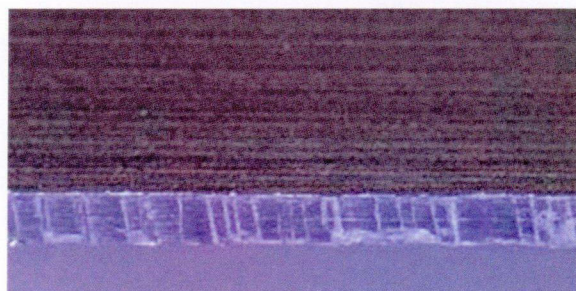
は Table 5-8 に示す加工条件で厚み 2 mm のアルミサッシ(材質 : JIS A4706) を溝加工し, その側面を観察した結果である。未処理の超硬合金製工具では 3000 個加工時点でバリの発生に加えて, 加工面品位が規格値を越えたが, DLC コーティングでは 8000 個加工時点においてもびびりもなく, 切削音も低い状態で加工面品位も良好な結果が得られ, 約 3 倍の工具寿命延長が図れた。
